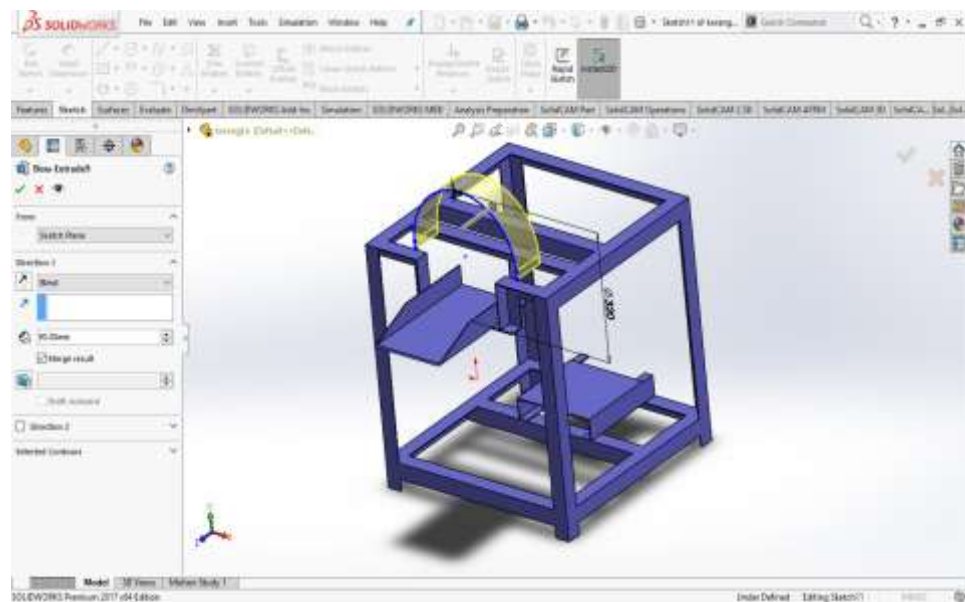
Extrude Pada Penampung Hasil Singkong
